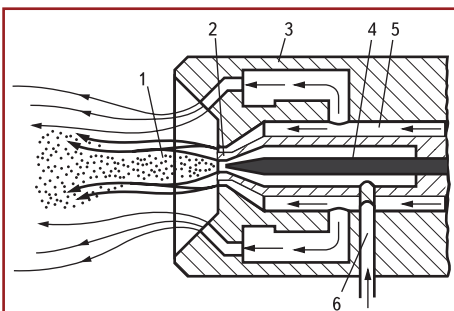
Схема нанесения ФР способом пневматического распыления: 1 – область разрежения; 2 – сопло; 3 – форсунка; 4 – регулирующая игла; 5 – распыляющий газ; 6 – подача ФР
